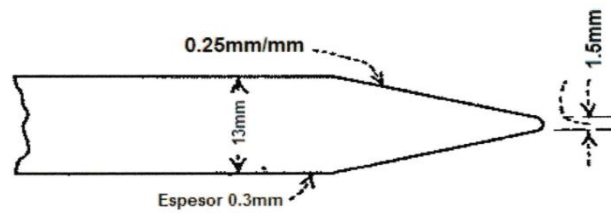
Calibrador de hoja para medida de grietas
